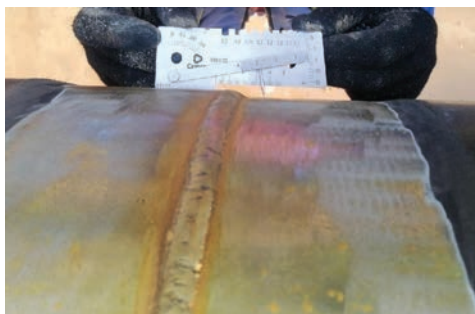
Контроль стыкового сварного шва трубопровода.
